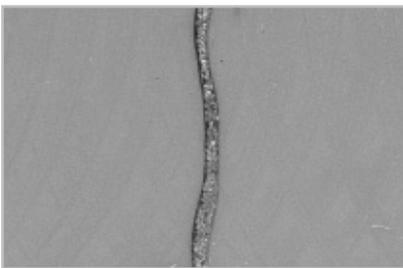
Разрез сварного соединения образца из PEEK
